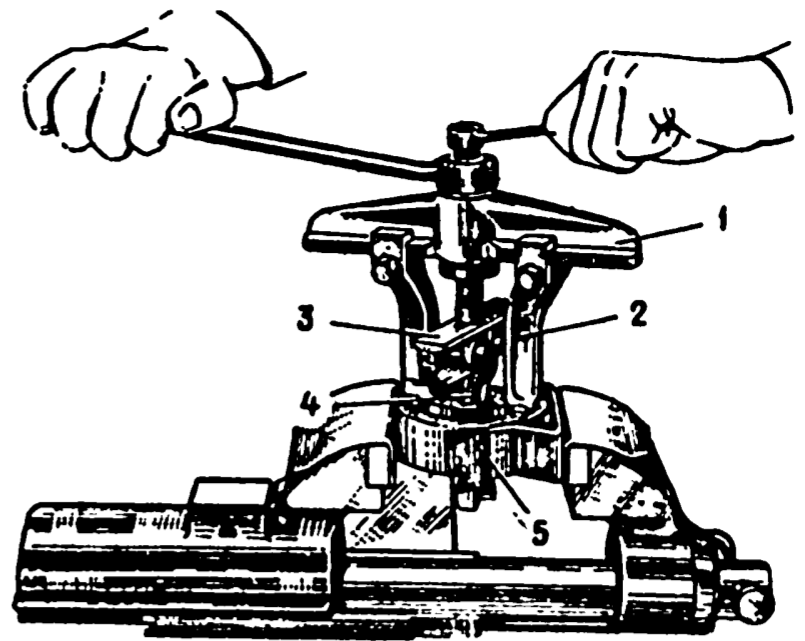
Выпрессовка подшипника из упругой опоры: 1 - планка А.40005/2; 2 - лапки А.40005/11; 3 - съемник А.40005/4; 4 - лапки; 5 - упругая опора
